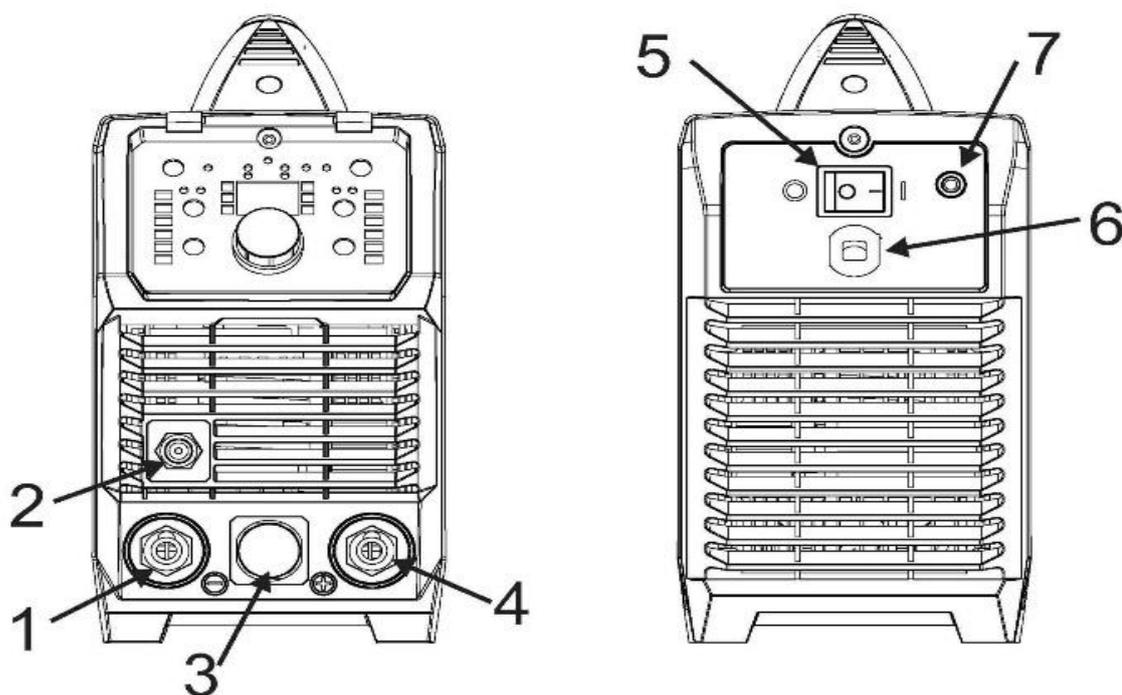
Vista Frontal e Traseira Joy TIG 230P AC/DC.
